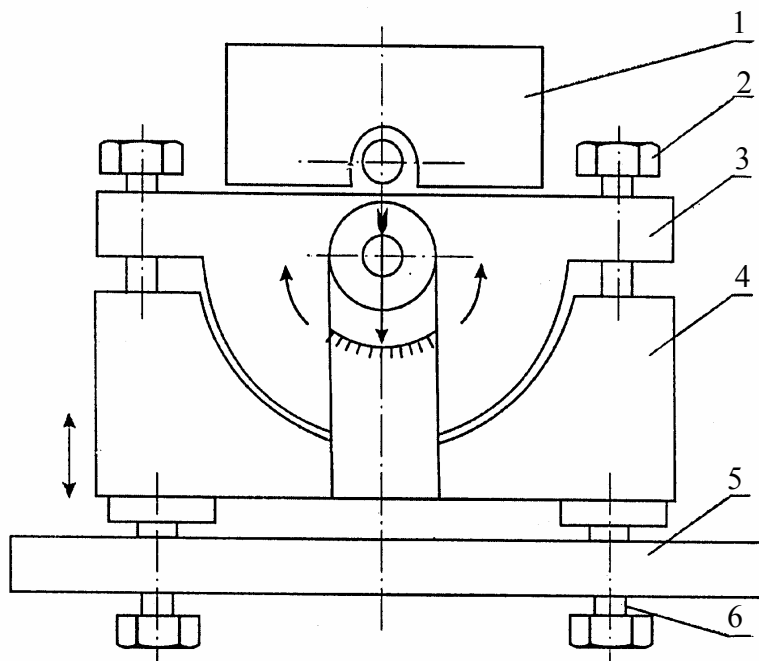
Схема стенда для імітації поздовжніх і поперечних кренів:
